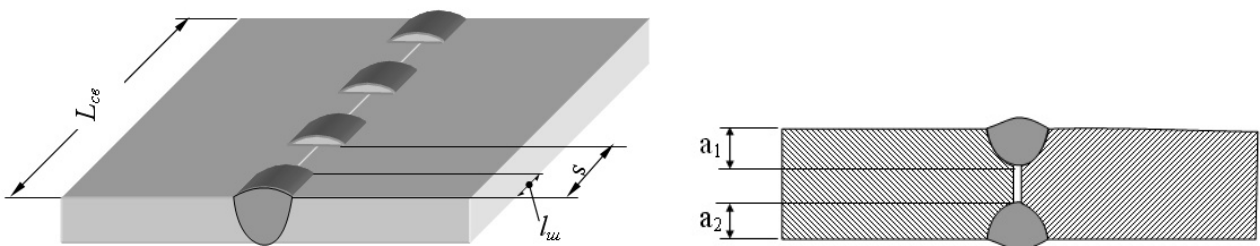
Сварные стыковые соединения с прерывистым швом
